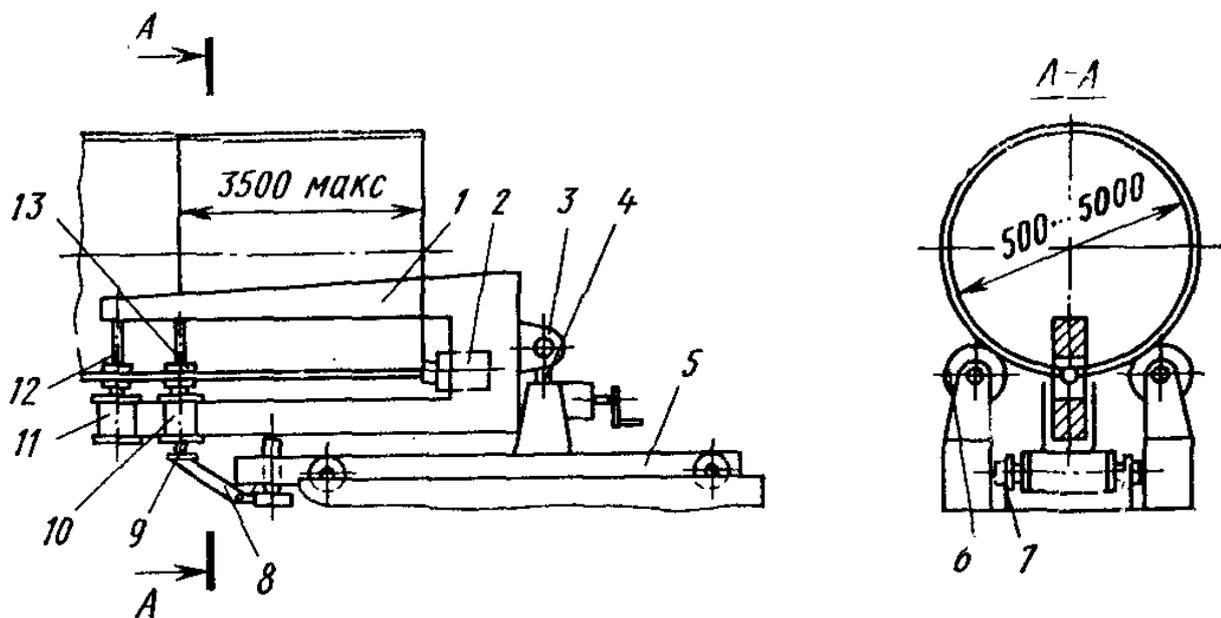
Установка для механизированной сборки кольцевых стыков цилиндрических сосудов
